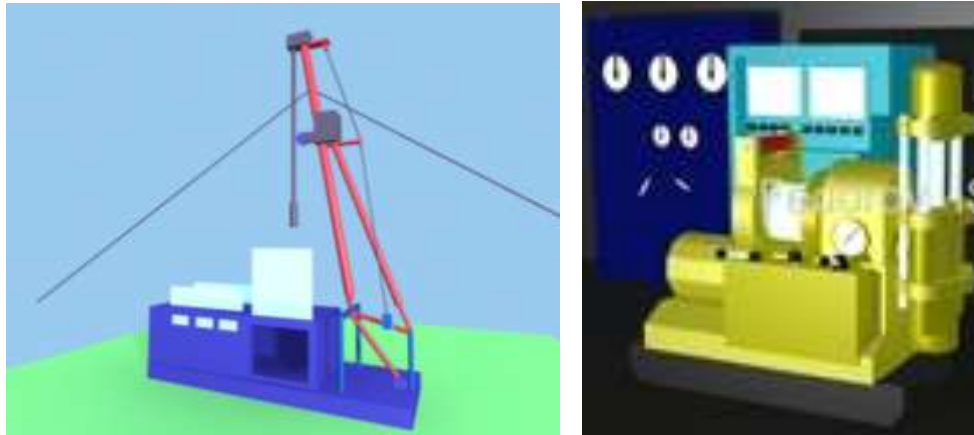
Загальний вигляд бурової установки УКБ-7П
